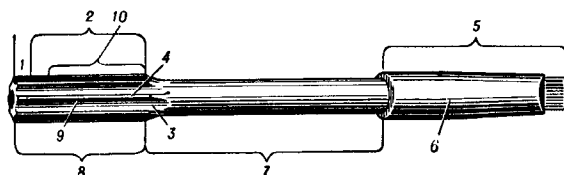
Элементы развертки: 1 — режущая часть; 2 — калибрующая часть; 3 — канавка; 4 — ленточка; 5 — хвостовик; 6 — конус; 7 — шейка; 8 — рабочая часть; 9 — ауг; 10 — обратный конус.
